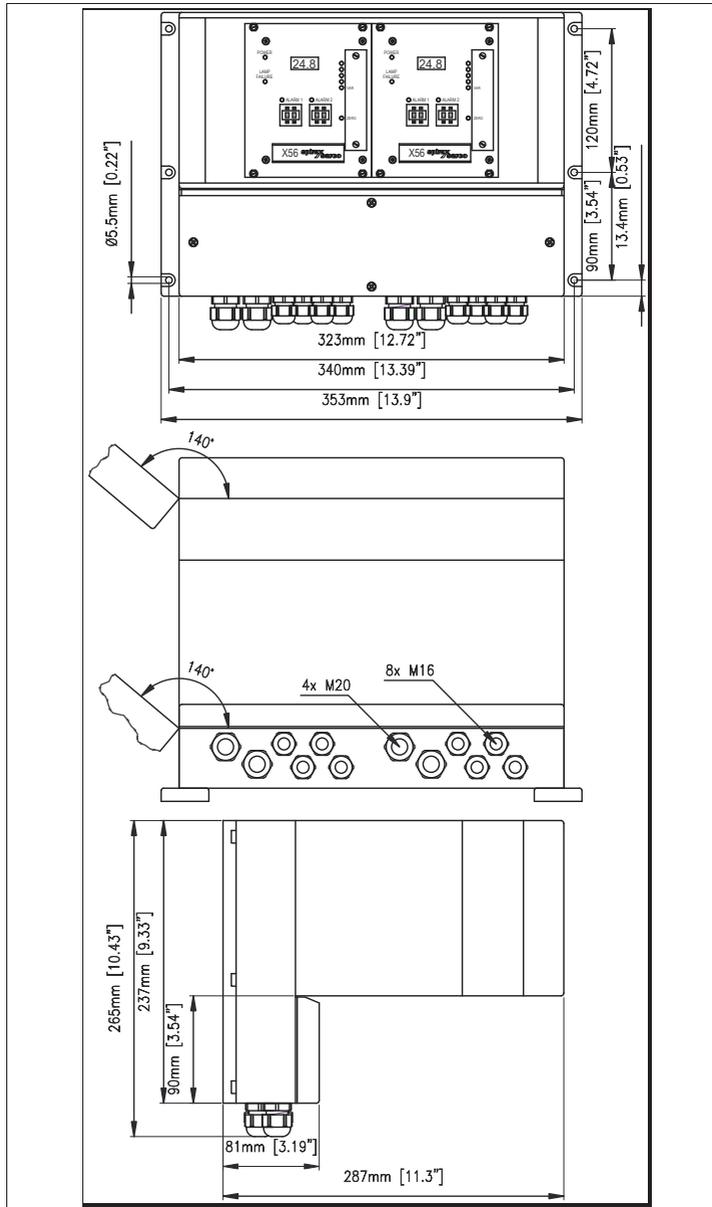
Dimensiones para la Caja B19-42 de montaje en pared.
